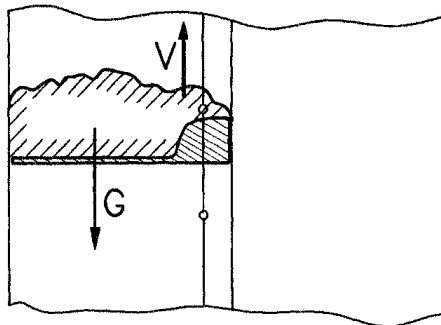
Компонувальна схема зі зміненою робочою поверхнею скребка зернового елеватора.
